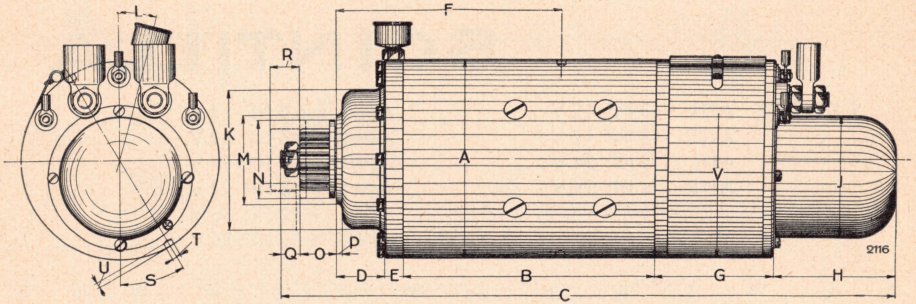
Dimensions d'encombrement pour démarreurs type AJ
